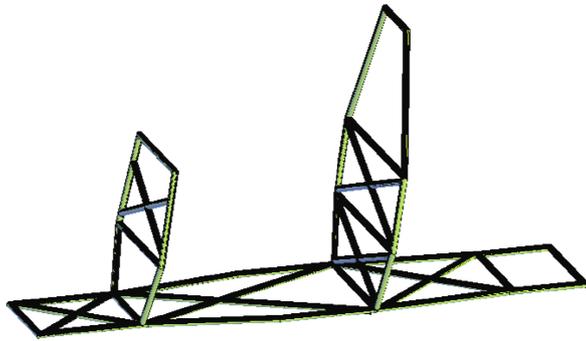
Vista 3D del soporte principal del chasis⁸⁸
